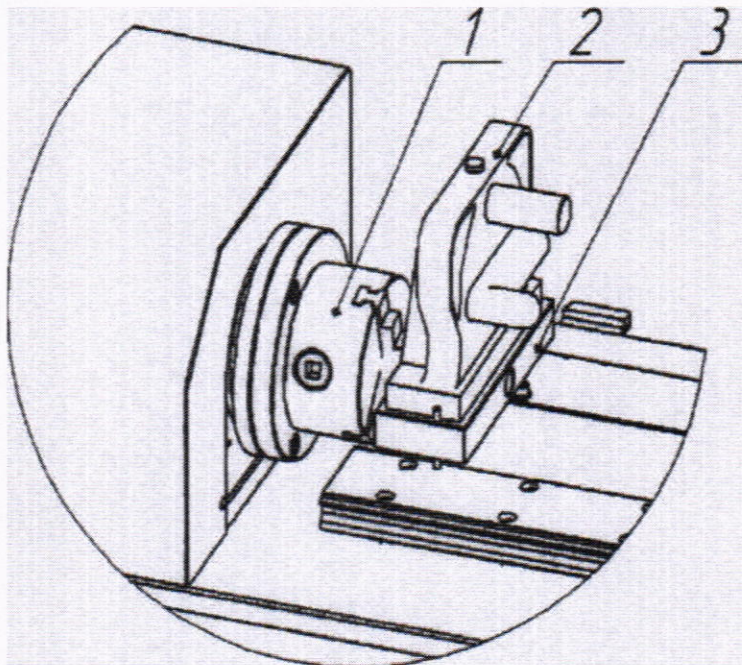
Схема установки приспособления для определения угла закручивания
